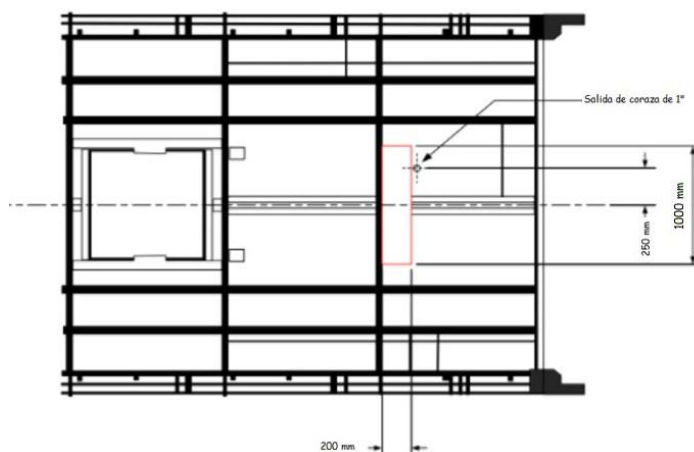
Refuerzo en carrocería para panel para información al pasajero
